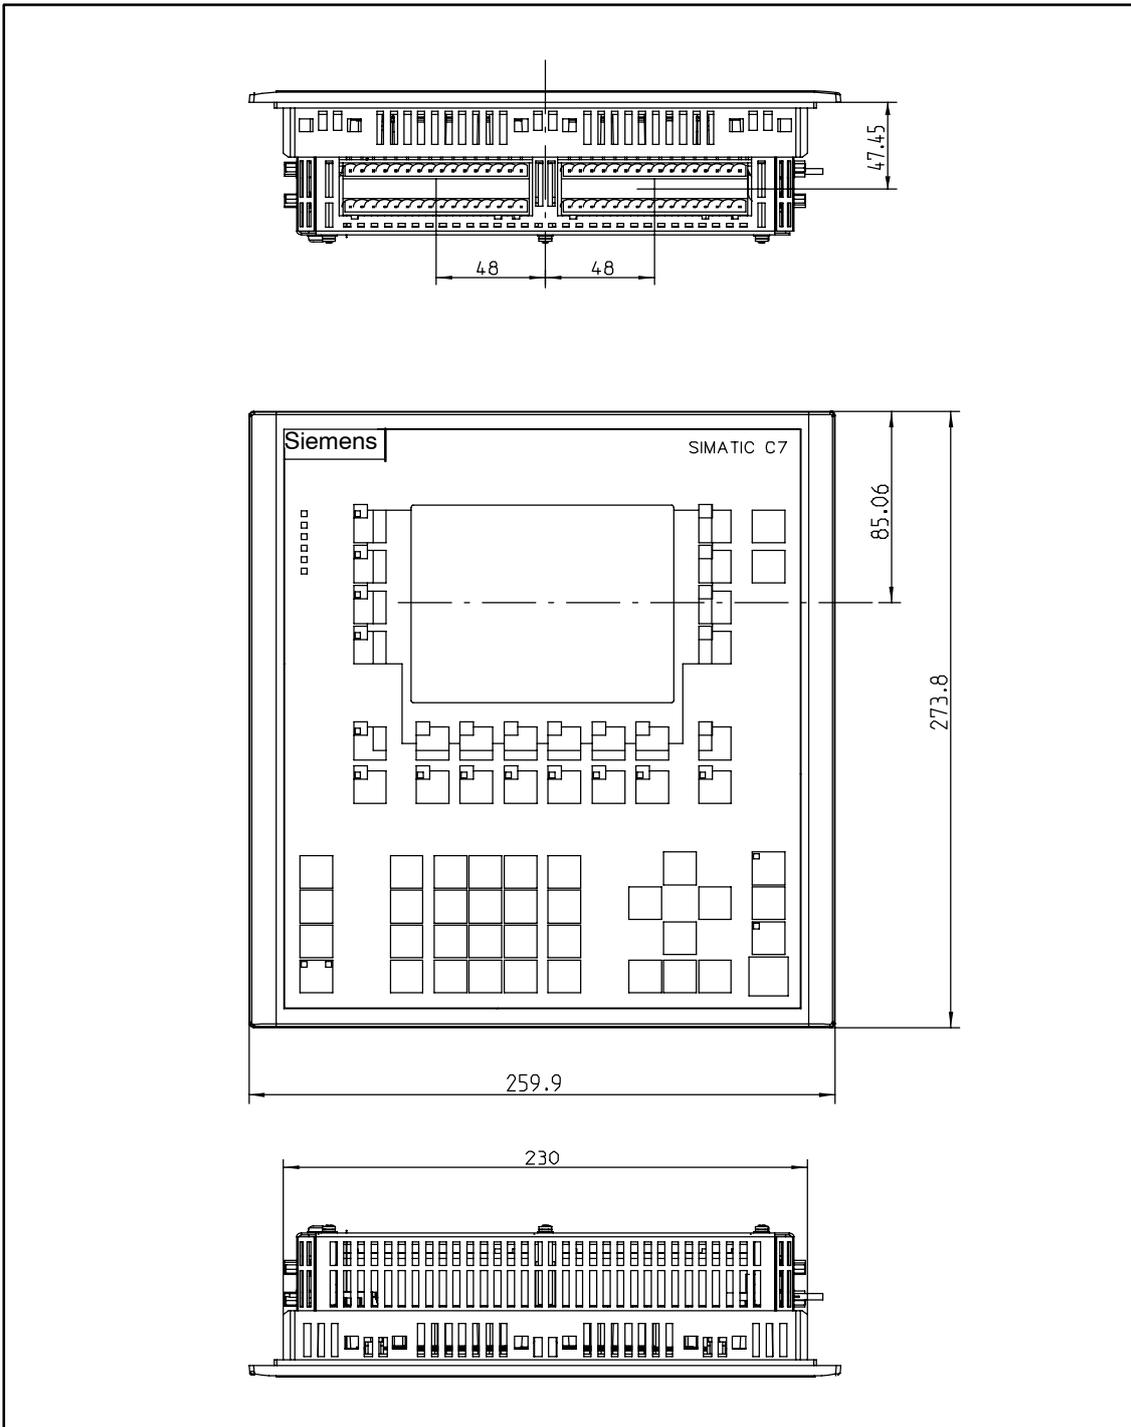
Maßbilder für das C7-635 Key (Maße in Millimeter)
